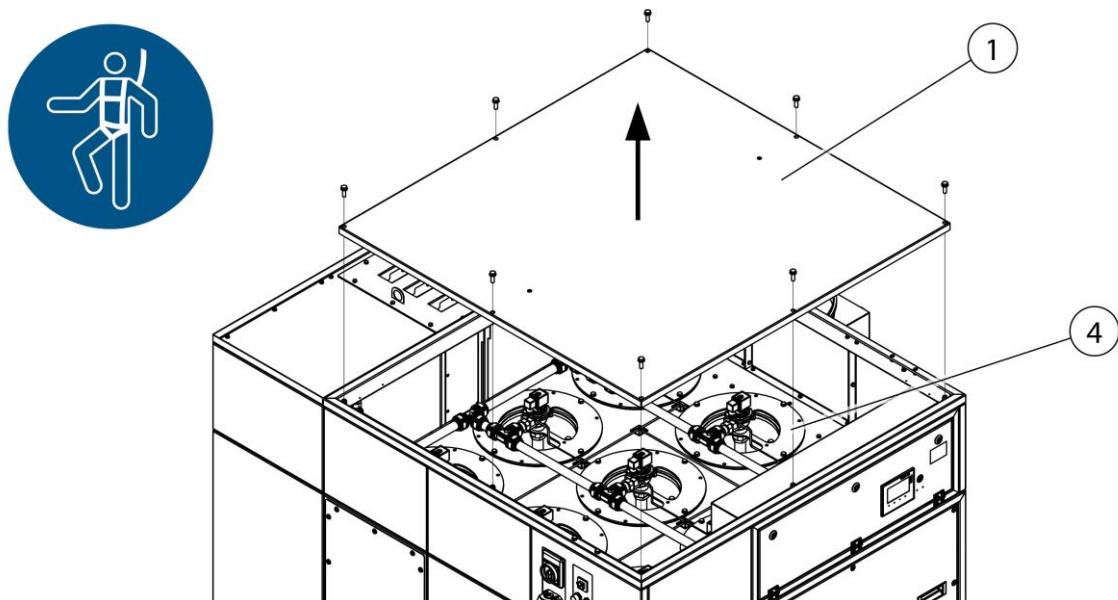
Remplacement du filtre – Démontage de la tôle de recouvrement
